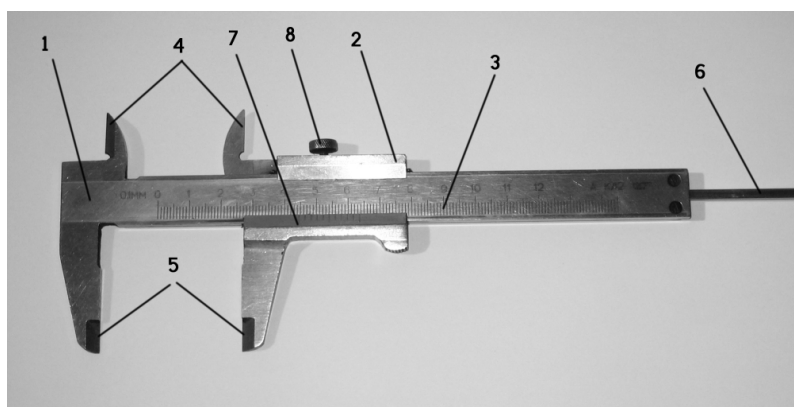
Штангенциркуль типу ШЦ-I:
